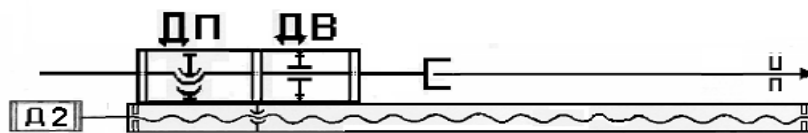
Схема привода ВПМ, работающего на общий суммирующий вал: ДВ – двигатель вращения со встроенной в вал ротора шлицевой втулкой; ДП – привод подачи со встроенной в вал ротора гайкой
